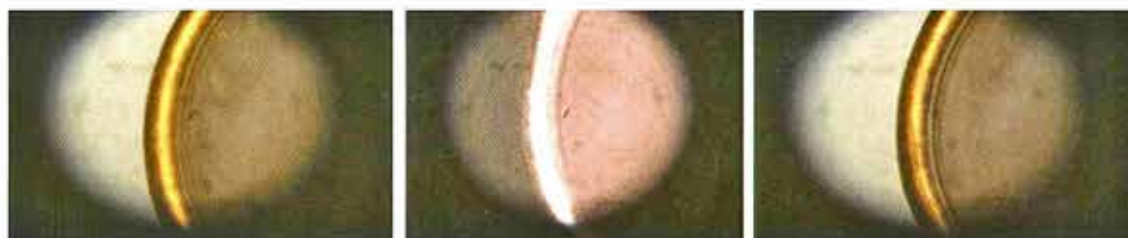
Cordón de soldadura del blanco anular desgasificado.
